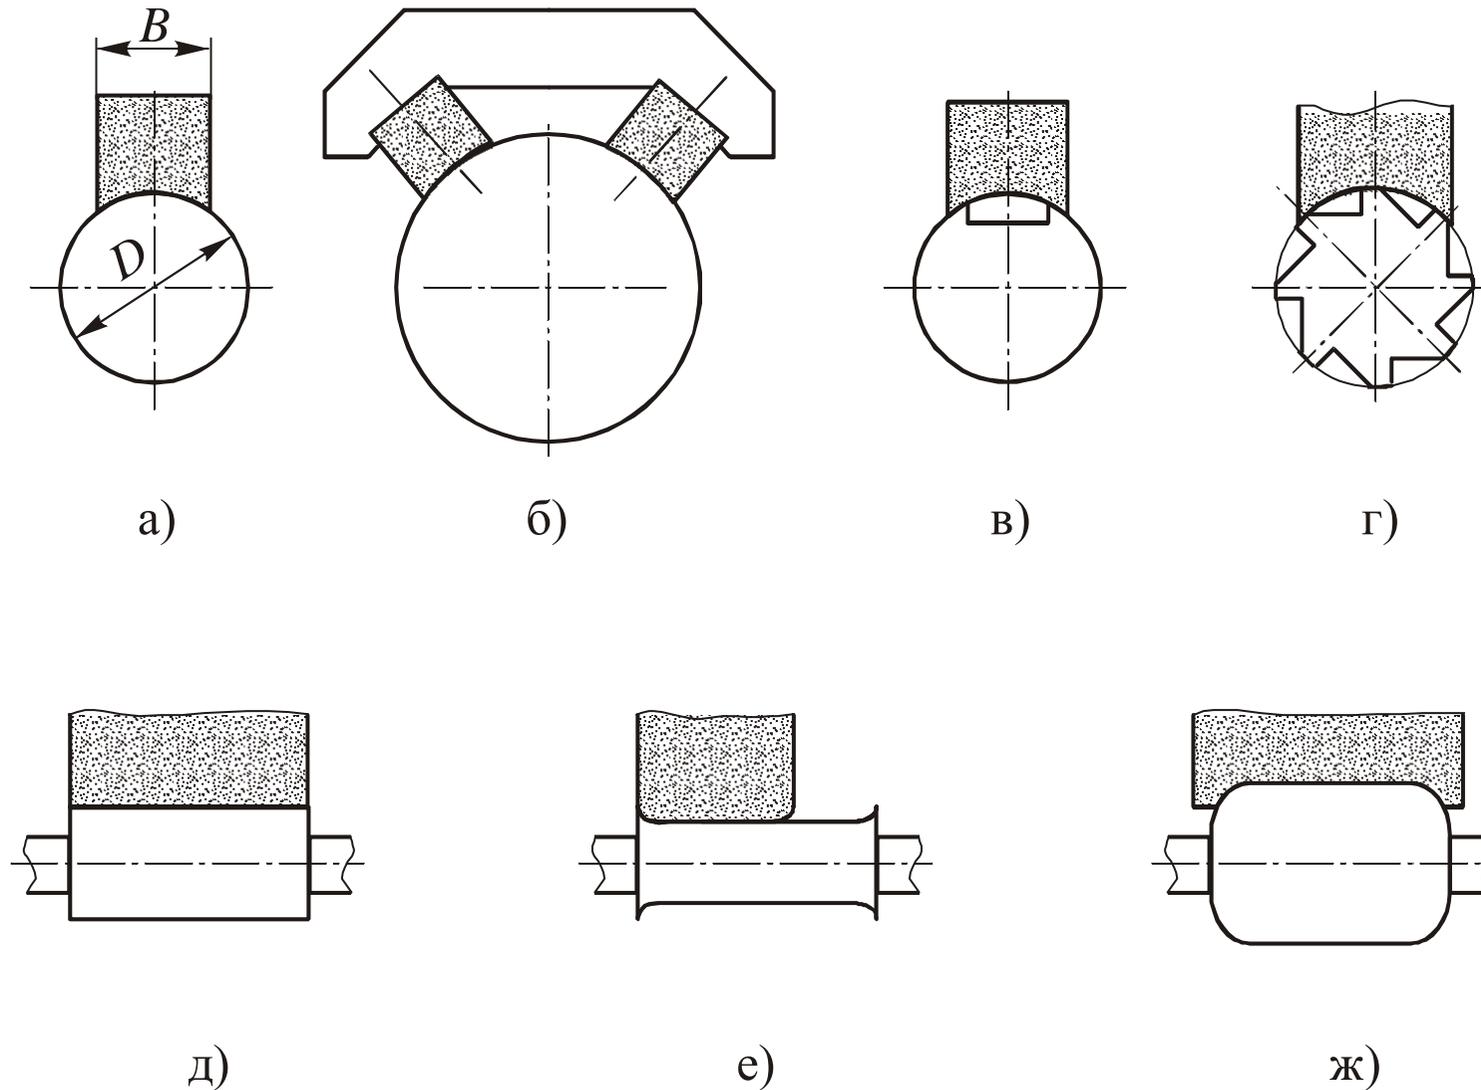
Формы и размеры рабочих поверхностей брусков для суперфиниширования: *а* – заготовка малого диаметра; *б* – заготовка большого диаметра; *в, г* – заготовки с пазами; *д...ж* – короткие заготовки
